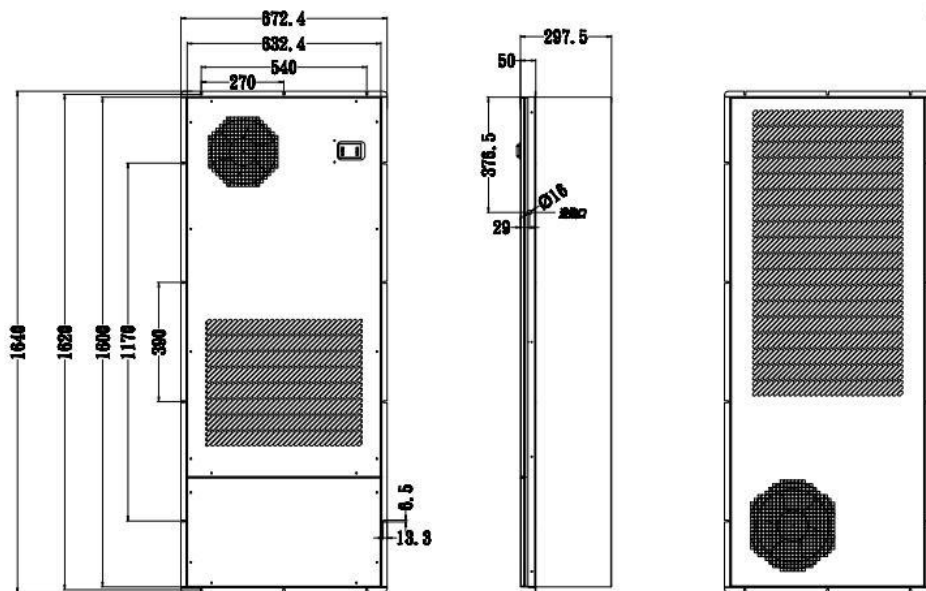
Габаритные размеры SNR-ACC-7000-ACH
